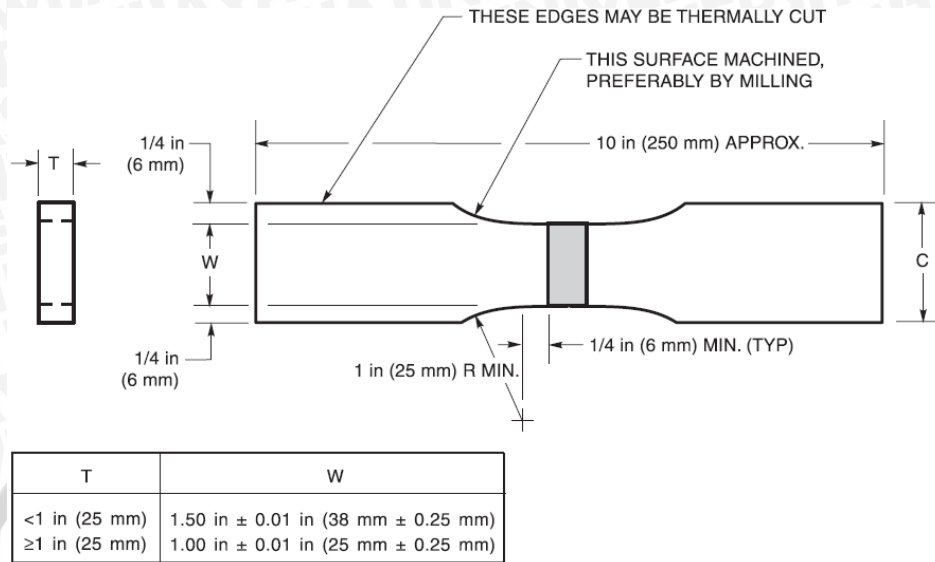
Dimensi benda kerja setelah proses pengelasan
